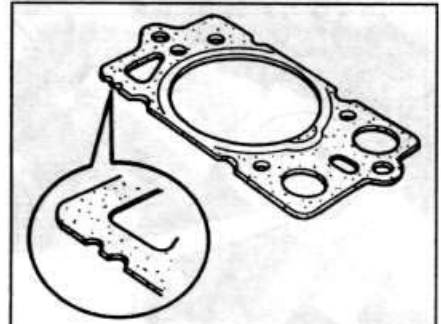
Маркировка прокладок головок цилиндров по толщине
